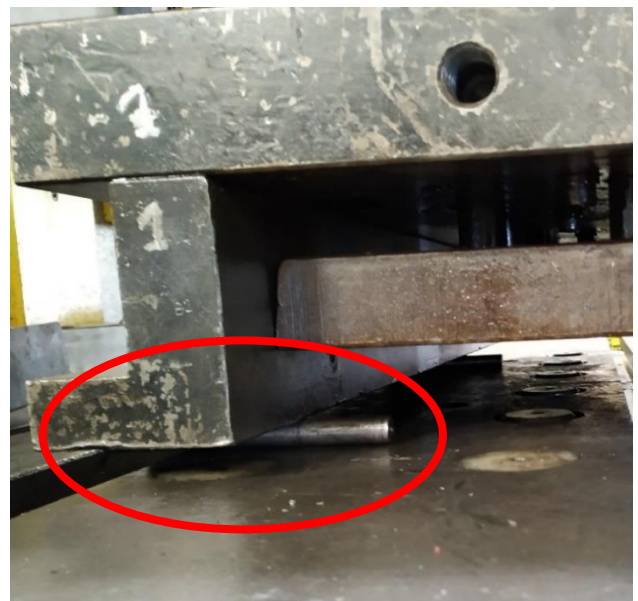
Barras de ferro utilizadas para posicionamento de ferramenta frontal
